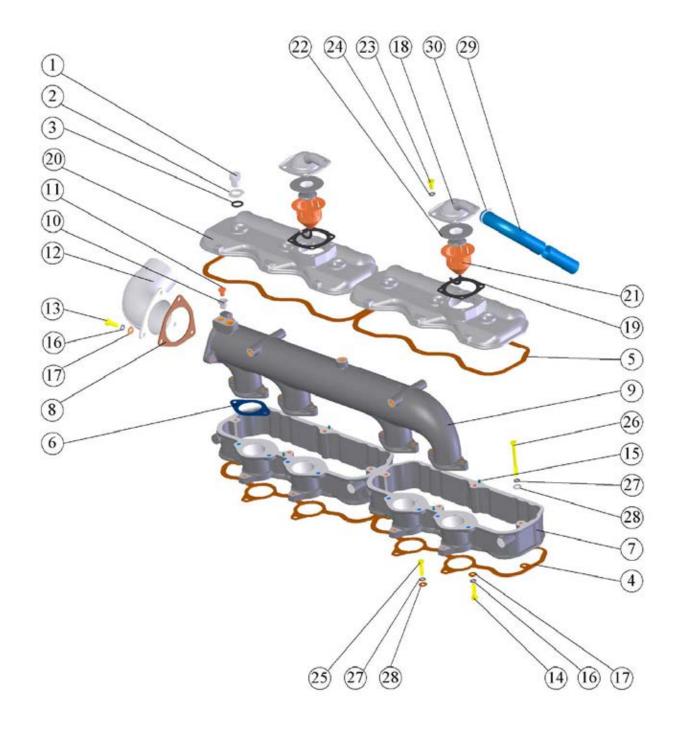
Крышки головок цилиндров, коллектор и сапуны
